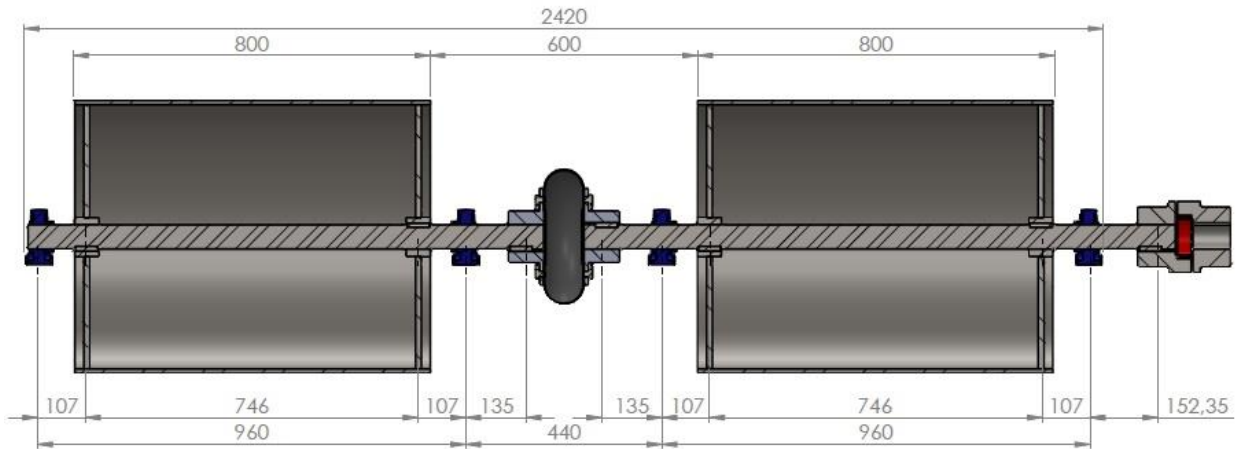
Ubicación componentes conjunto dinamómetro
